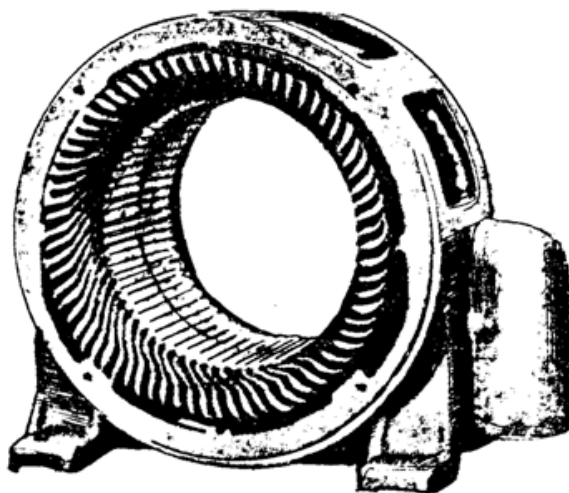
ESTATOR DE UN MOTOR TRIFASICO MOSTRANDO LA UBICACION DE LAS BOBINAS.
